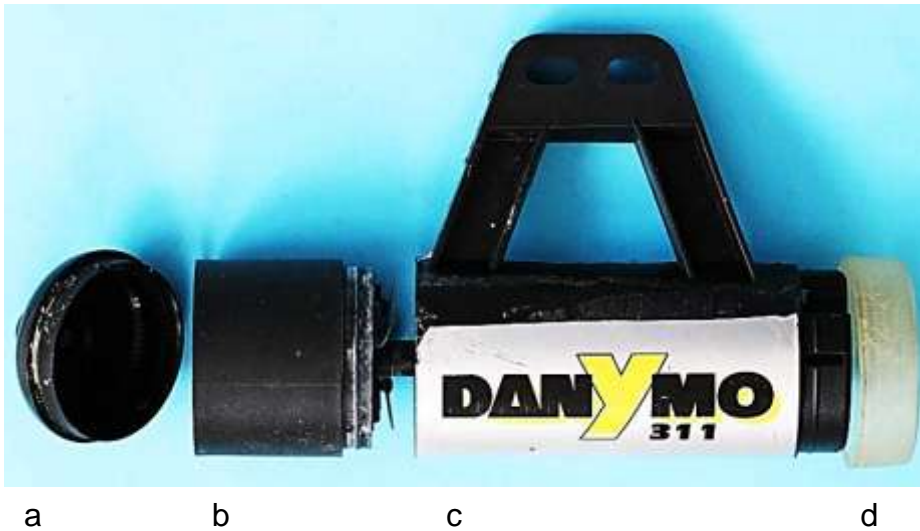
Gehäuseteile: a) Gehäusedeckel mit Hohlrund, b) Generatorgehäuse, c) Akkugehäuse mit Halterbügel, d) Gummidichtung
